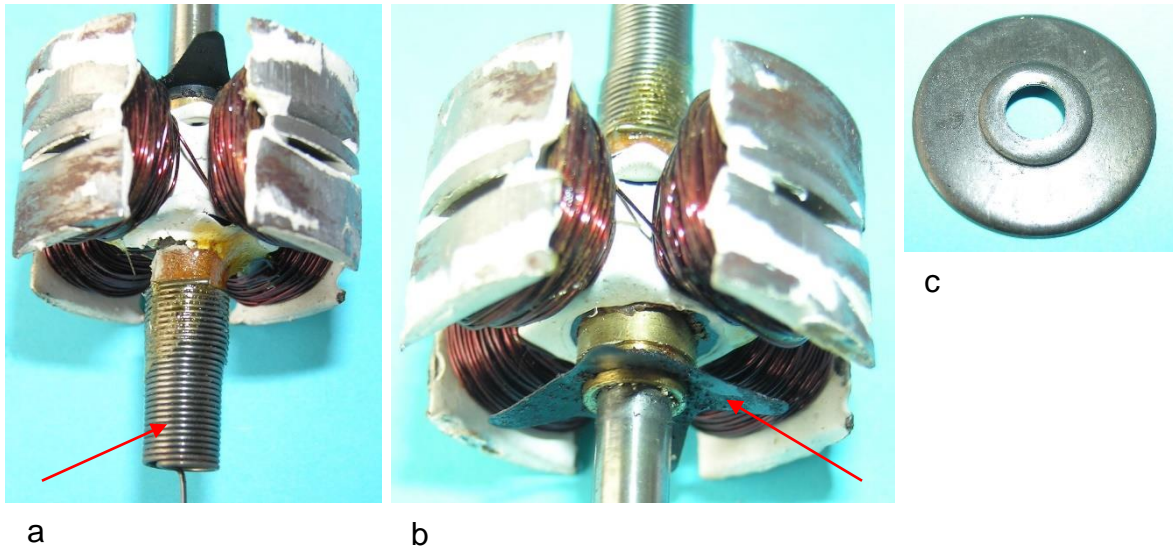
Stirnseiten des Ankers: a) Bürstenfeder auf dem Wellenstumpf, b) Blattfeder für den Axialspielausgleich, c) Anlaufscheibe
